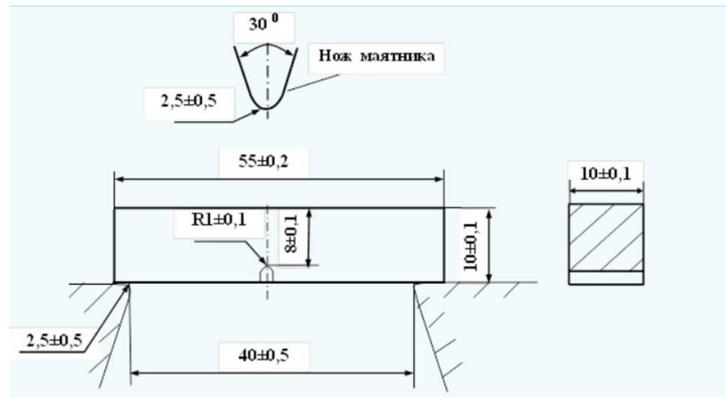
Форма и размеры образца для испытаний на ударную вязкость
